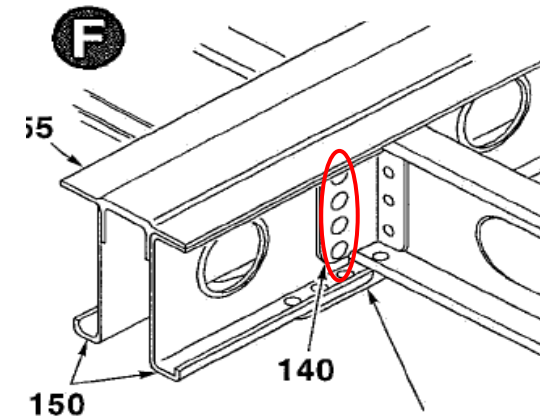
Detail F, mit dem Single Lap Joint bestehend aus 4 Nieten
